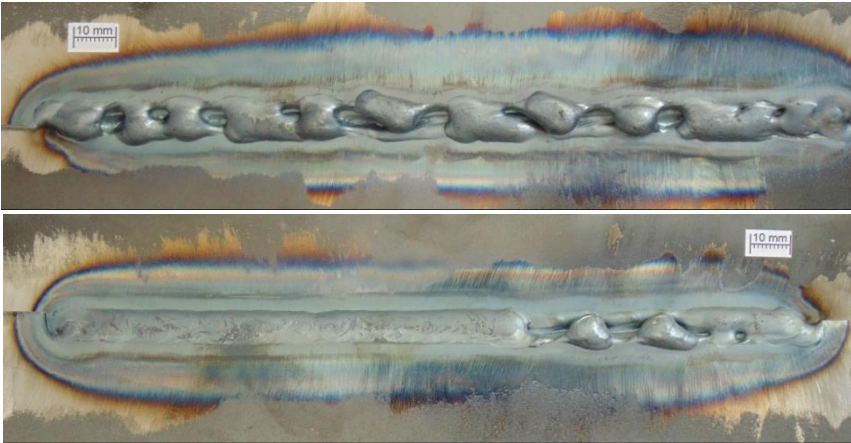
Soldagem de chapas sobrepostas com movimentação linear
